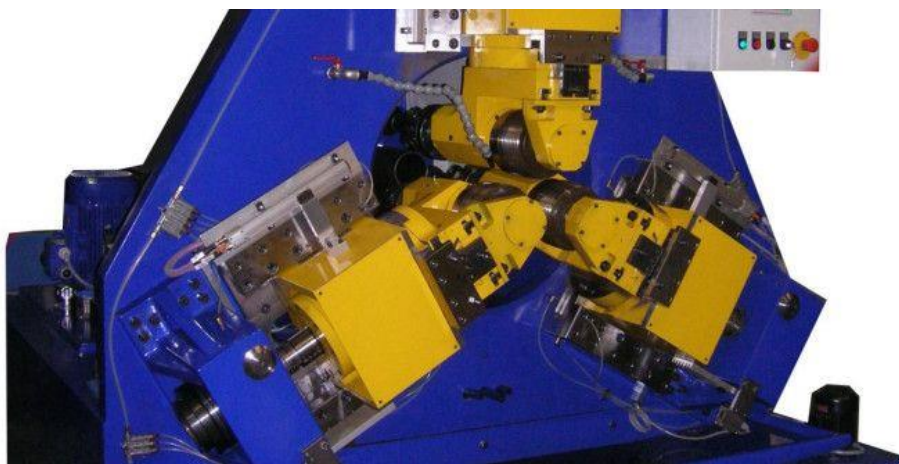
Резьбонакатной трехвалковый станок
